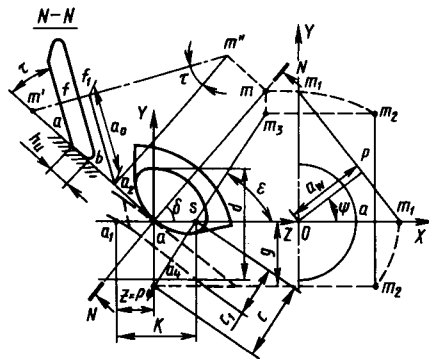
Определение параметров положения инструмента относительно заготовки
